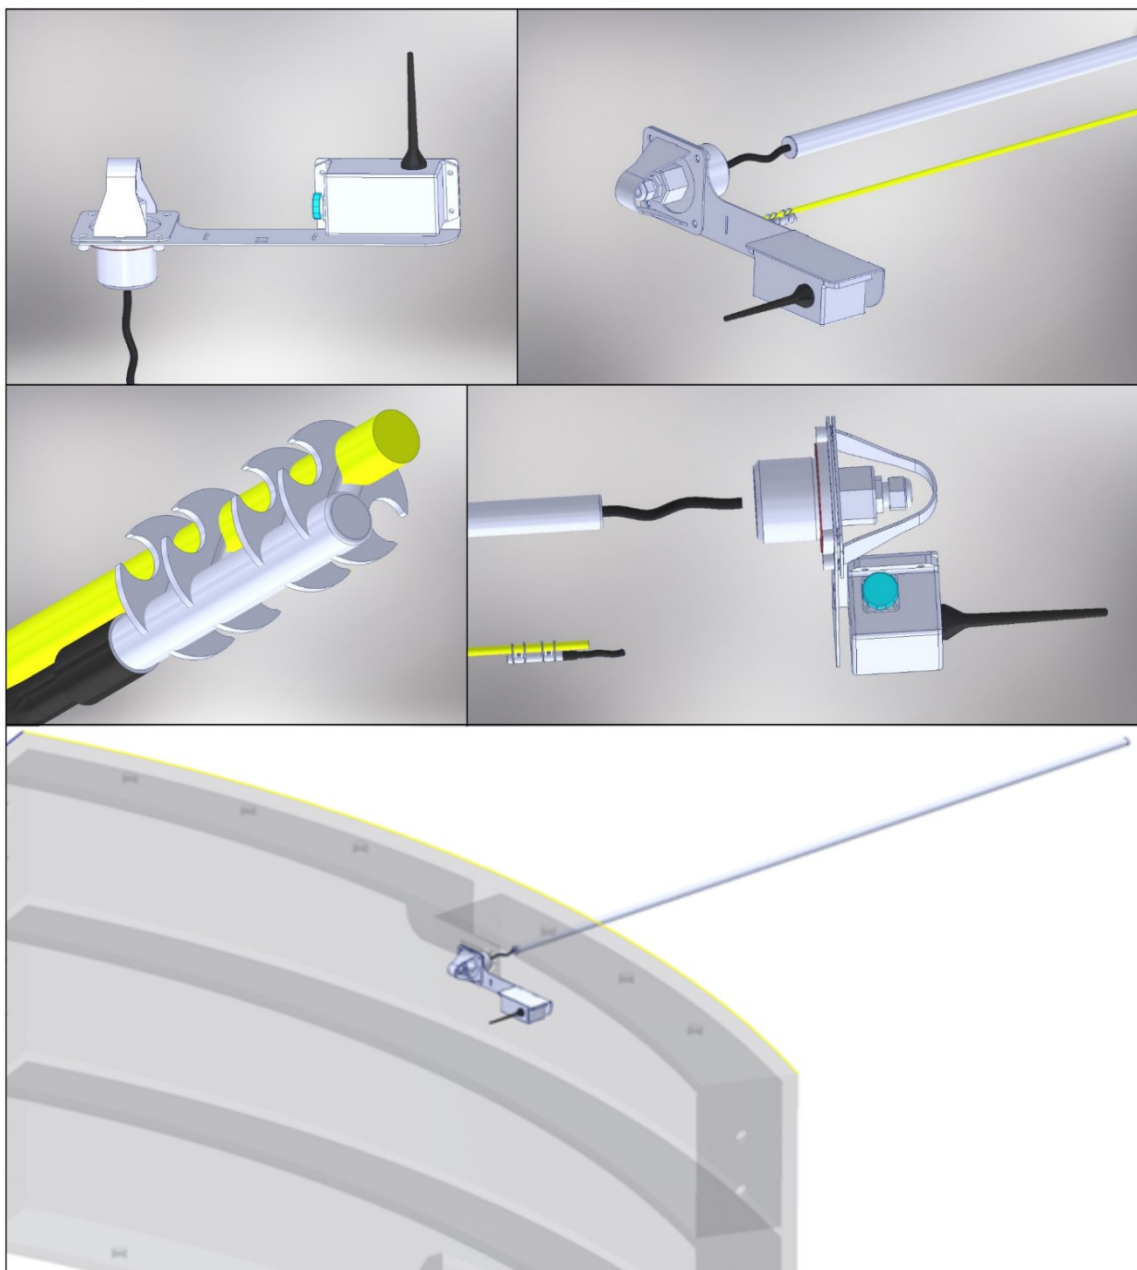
Элементы конструкции и внешний вид цифрового термометрического датчика
